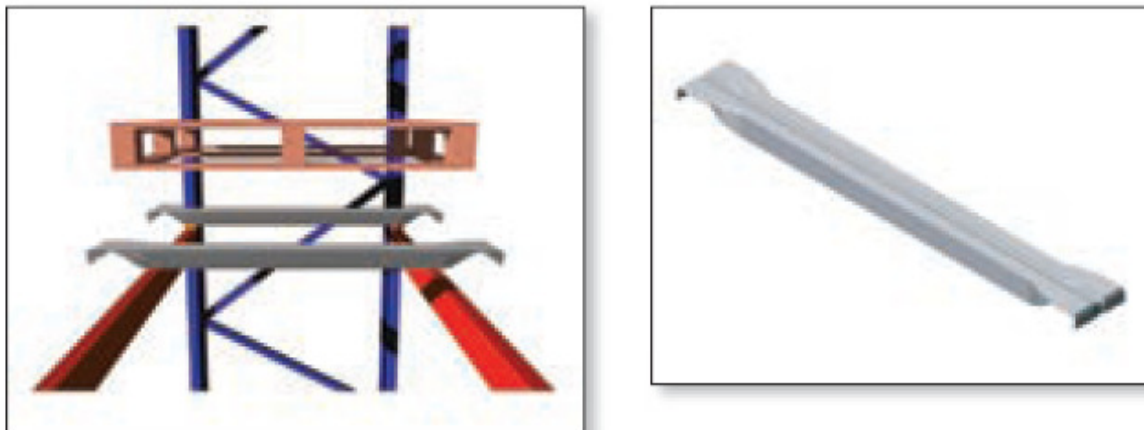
konstrukční řešení paletových regálových systému, [9]
